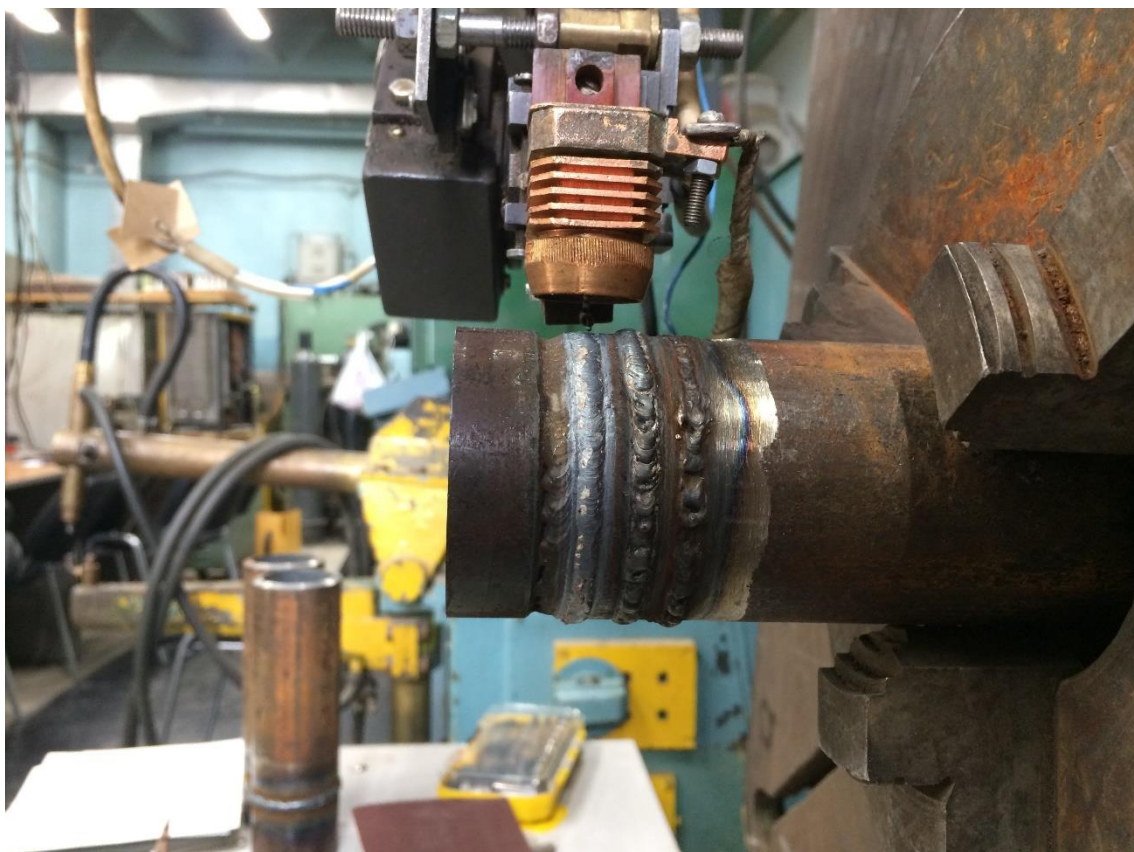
Итоговое приближение выбора способа наплавки
